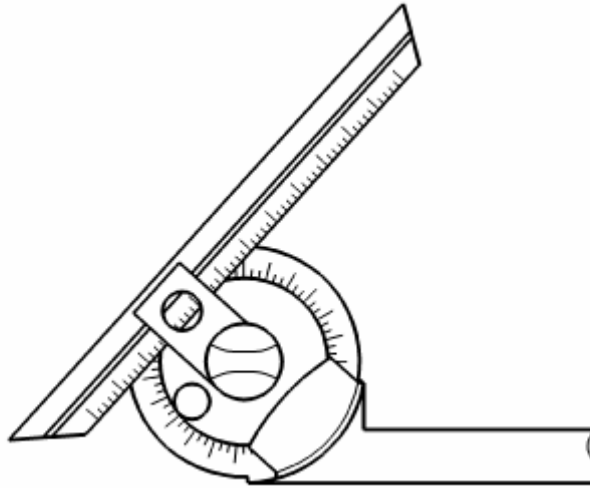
Кутмір з обертовою лінійкою для точного вимірювання кутів.
